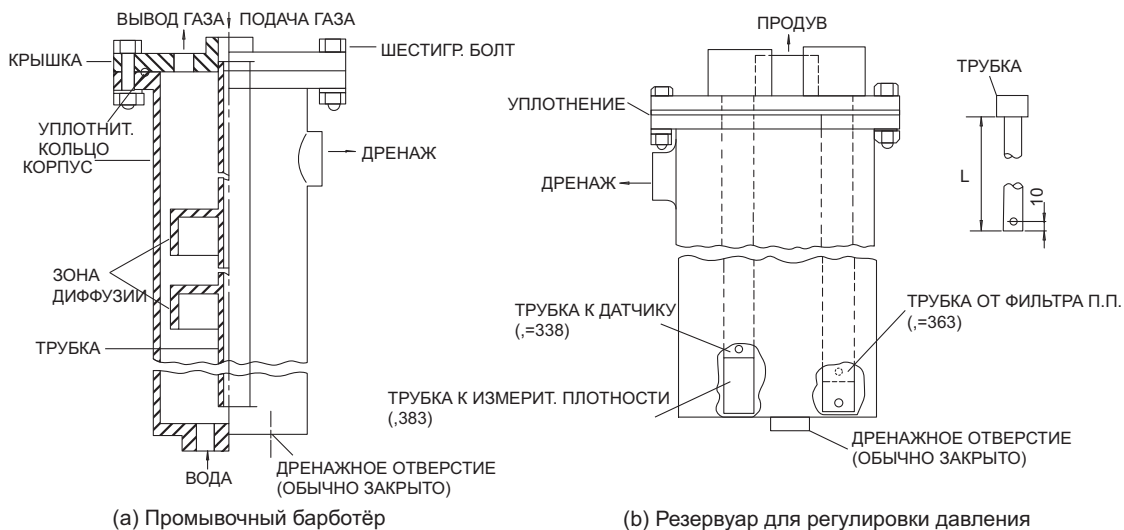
Промывочный барботёр и резервуар для регулировки давления
